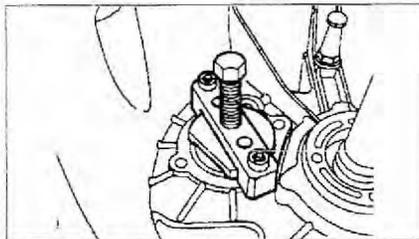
Закрепите зажим на корпусе коробки передач двумя болтами.
